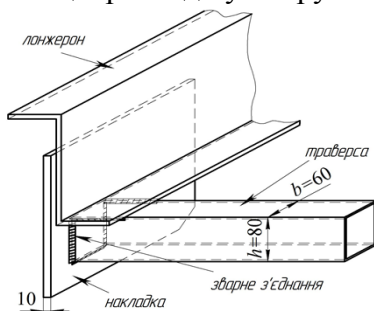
Схема зварного з'єднання поперечини з лонжероном
